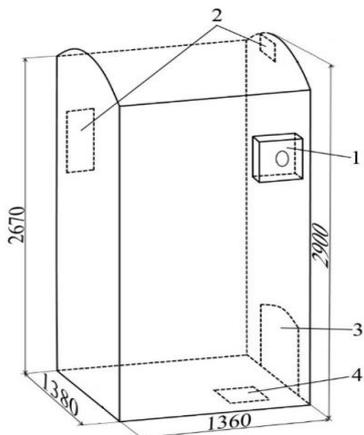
Схема топки котла (размеры в мм). 1 – короб форсунки; 2 – окна для подачи воздуха; 3 – вывод дымовых газов; 4 –летка ШЗУ
